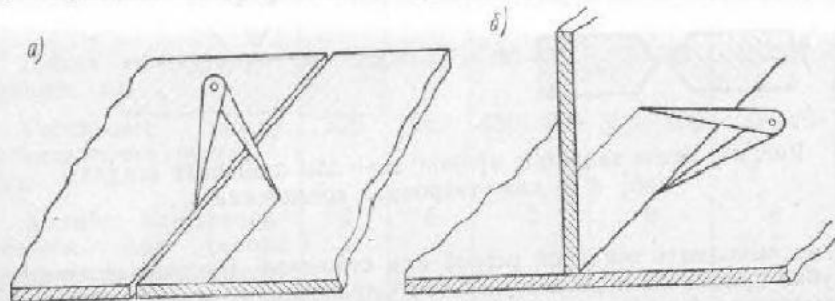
Причерчивание припуска: а — стыкование кромок; б — притыкание кромок.
